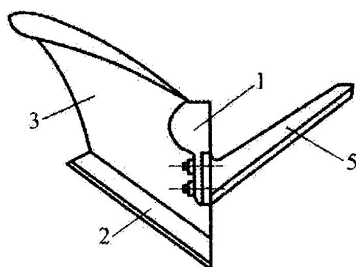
Корпус плуга, оснащений плоскорізною лапою:
